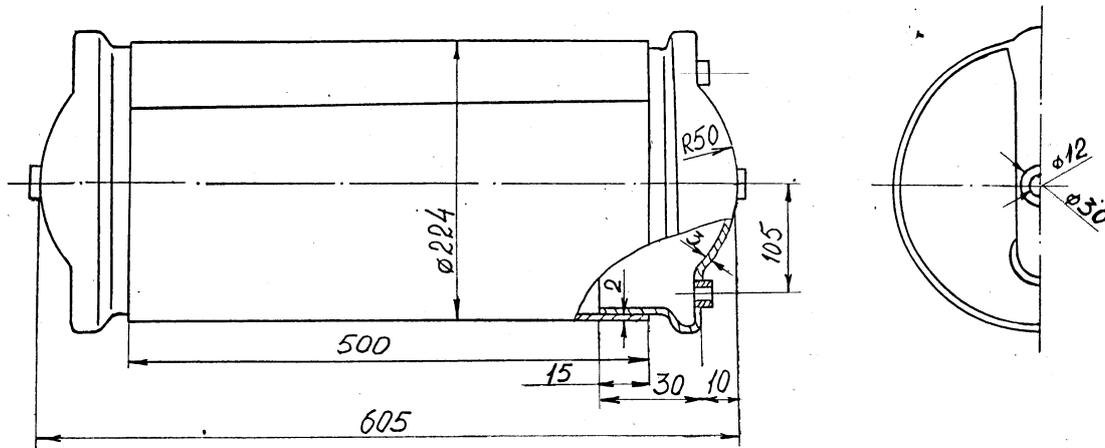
Схема флюсоремной подушки для сварки кольцевых швов
